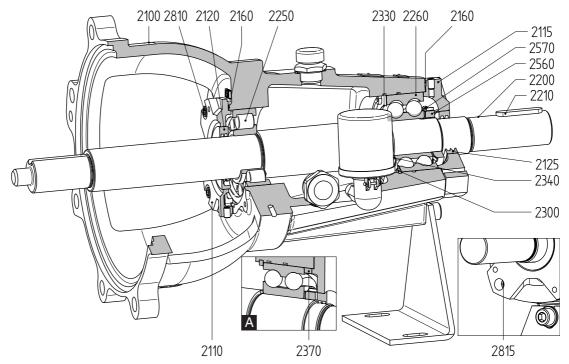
Palier L4 (renforcé, huilé) (A = groupe de palier 3).
